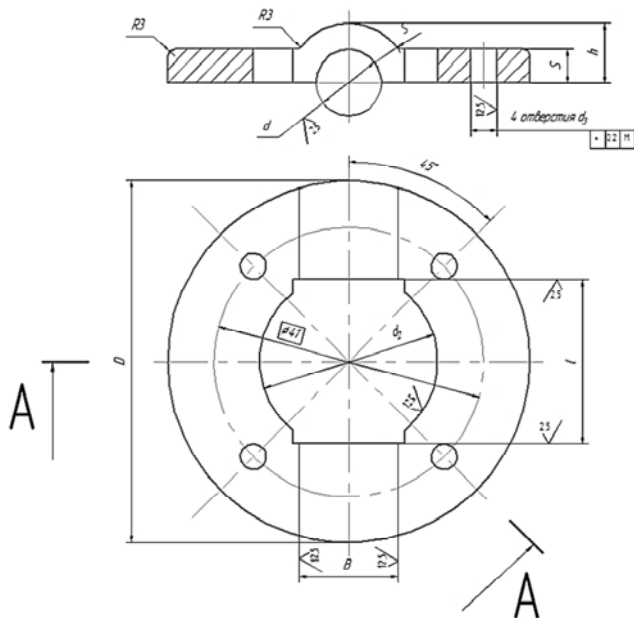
Конструкция крышки гидравлического приспособления для удаления стержней
